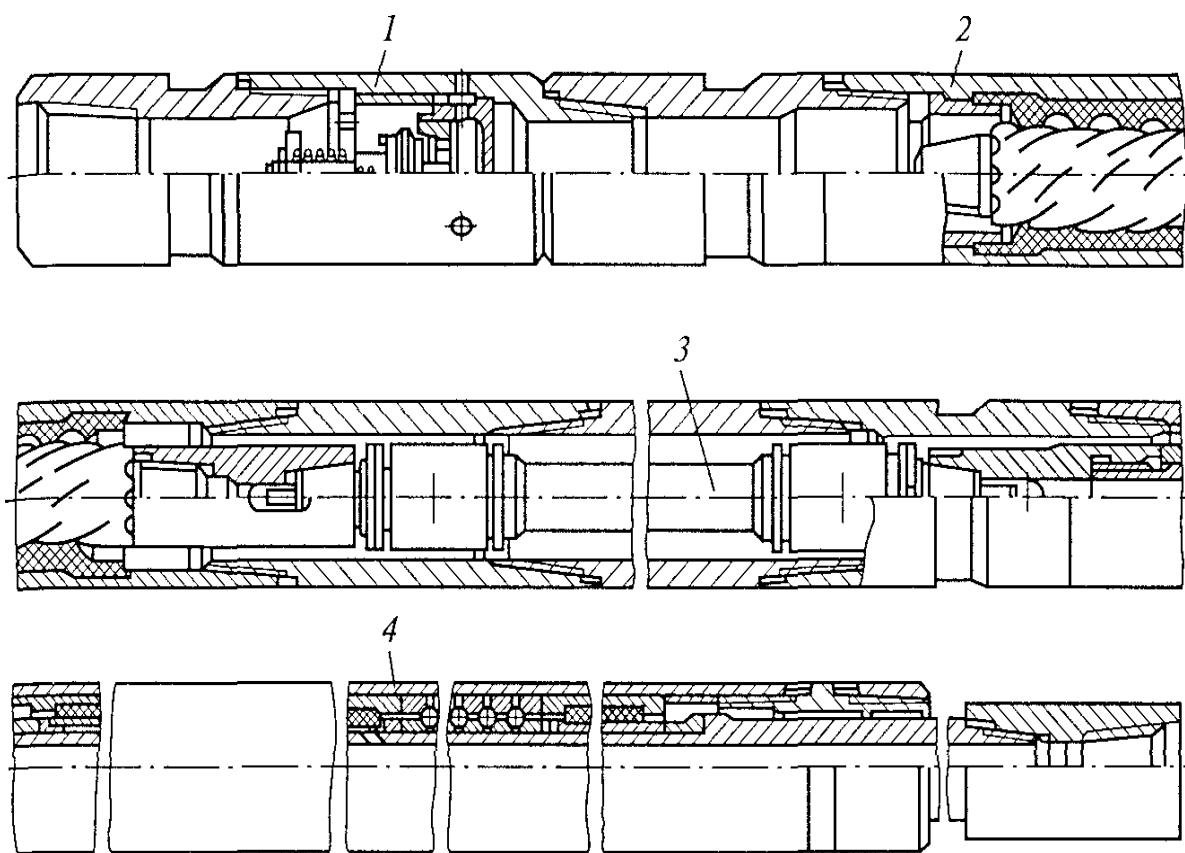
Винтовой (объемный) забойный двигатель Д1-195:
